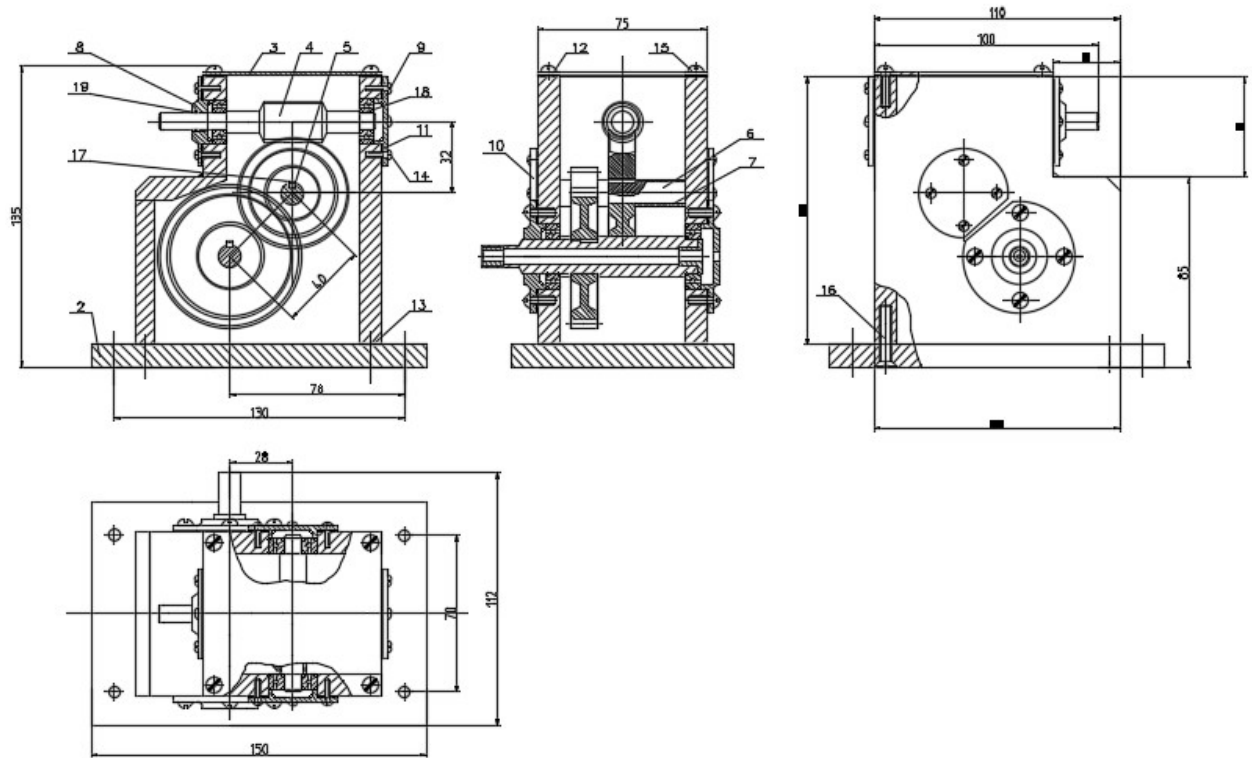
Ескіз редуктора черв'ячно-циліндричного.
